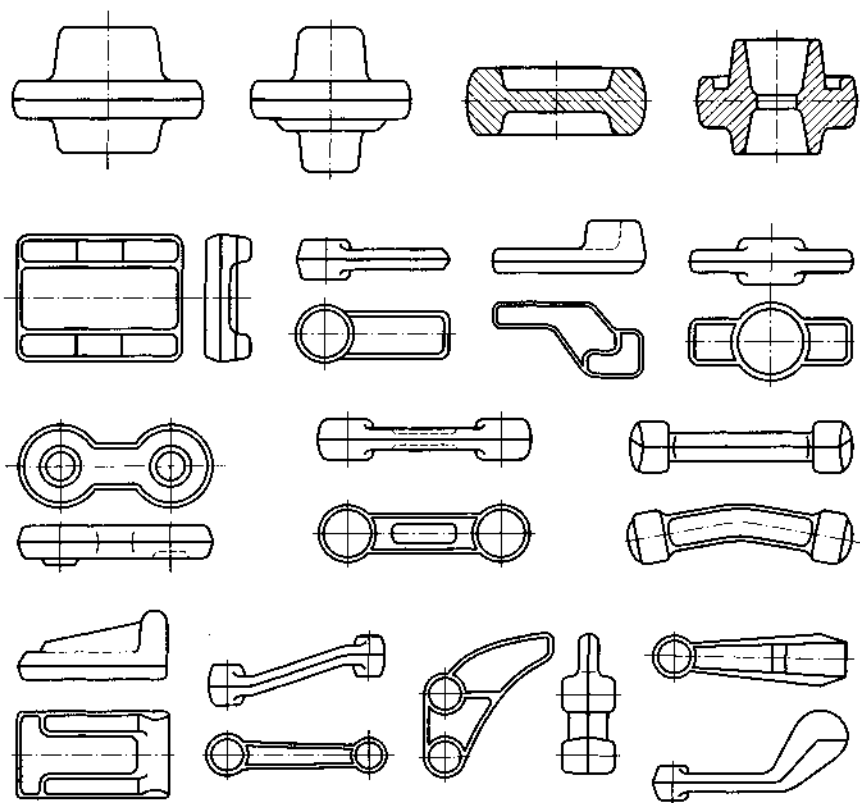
Типовые заготовки, изготавливаемые на прессах
